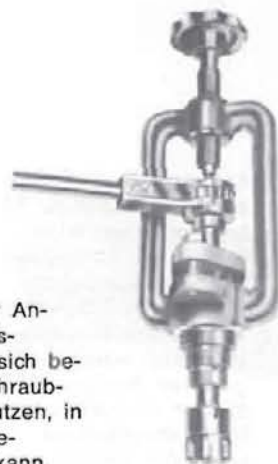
Anbohrapparat für Anbohrungen an Gasleitungen. Eignet sich besonders für Aufschraub- und Aufschweißstutzen, in die er direkt eingeschraubt werden kann.
